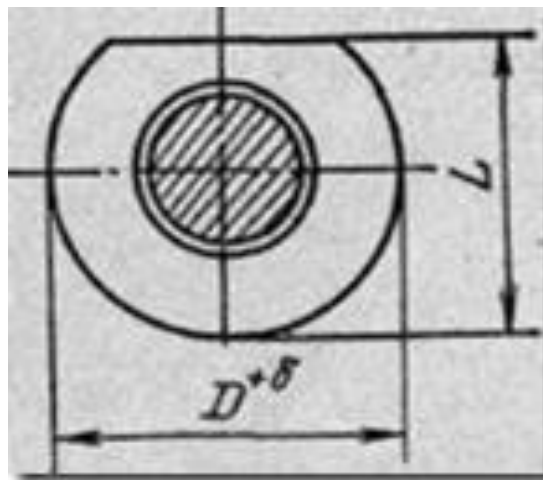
Схема возникновения погрешностей при установке детали на цилиндрическую поверхность (палец)
